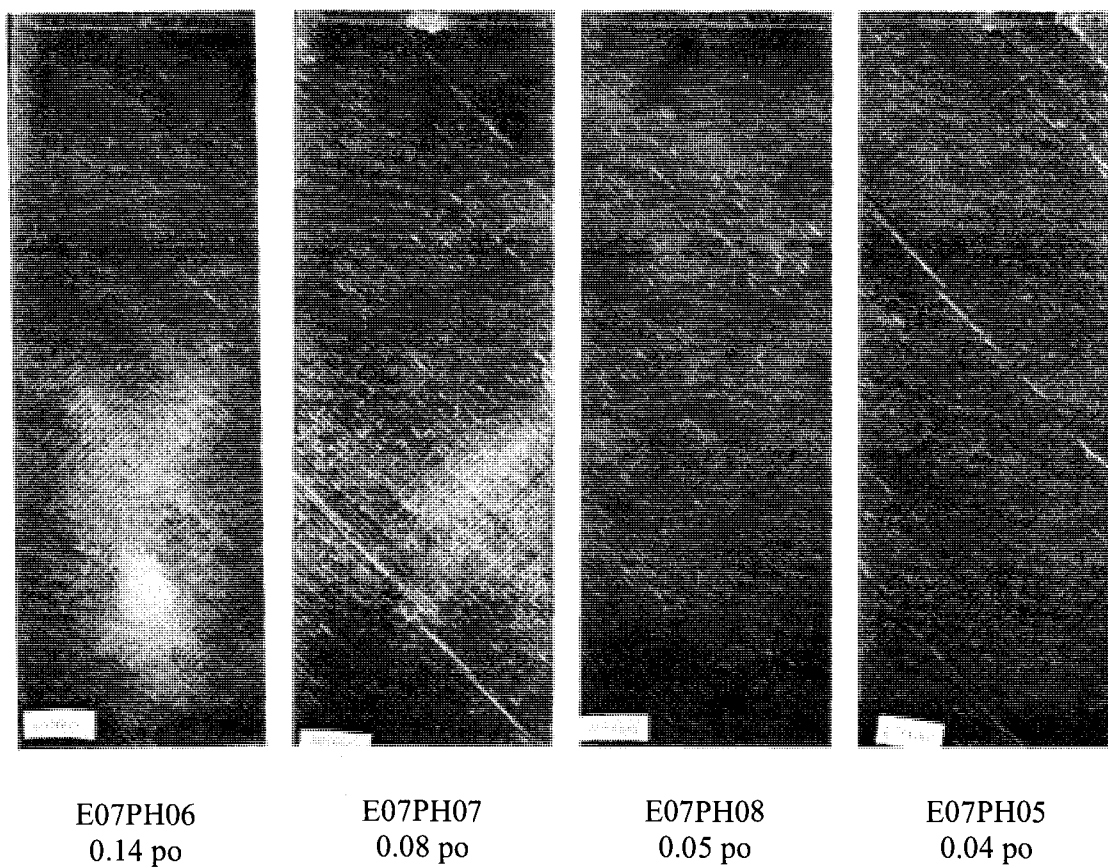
Pièces finales vue côté moule pour différentes épaisseurs de cadres.
